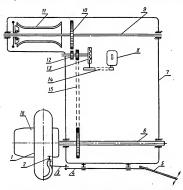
Схема специального станка для обрезки бортов и расслоения покрышки:
